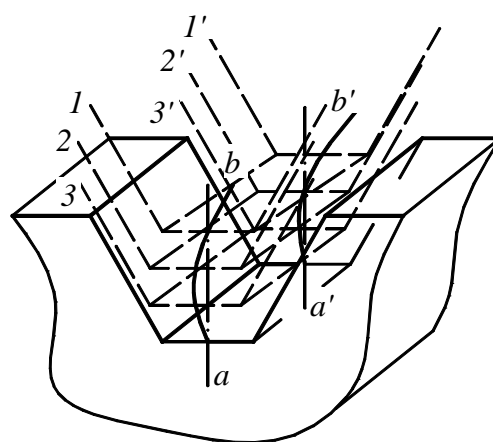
Пространственная схема снятия припуска при обработке торцовых зубчатых контуров по схеме с непрерывным движением деления
